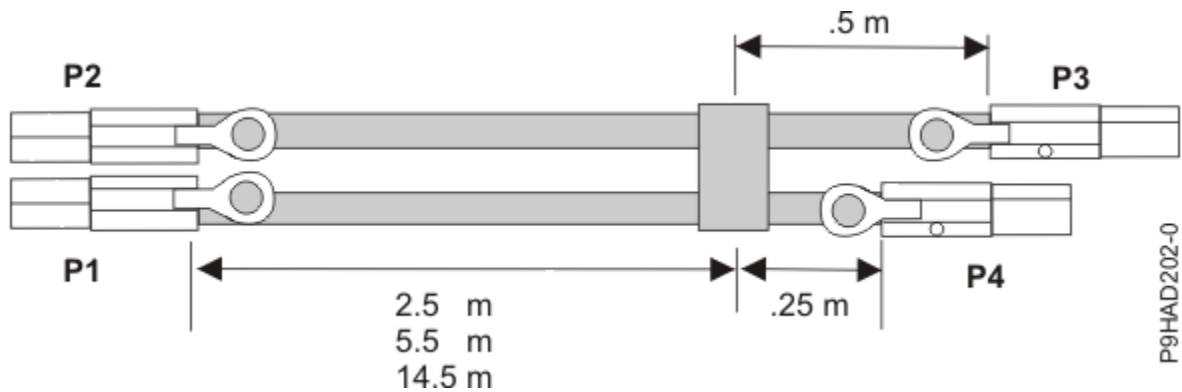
Longitudes de cable de conjunto de cables YO SAS externo
